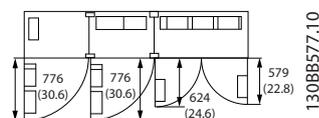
Пространство перед корпусом IP21/IP54, типоразмер F13
